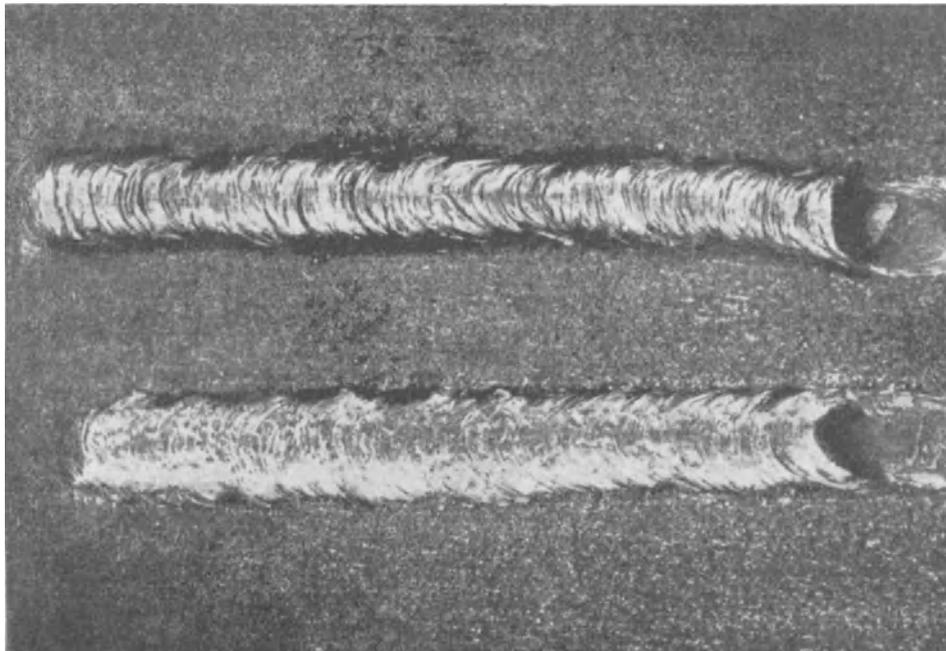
Schweißraupen einer dick (unten) und einer leicht ummantelten Elektrode (oben) bei gradliniger Elektrodenführung.
